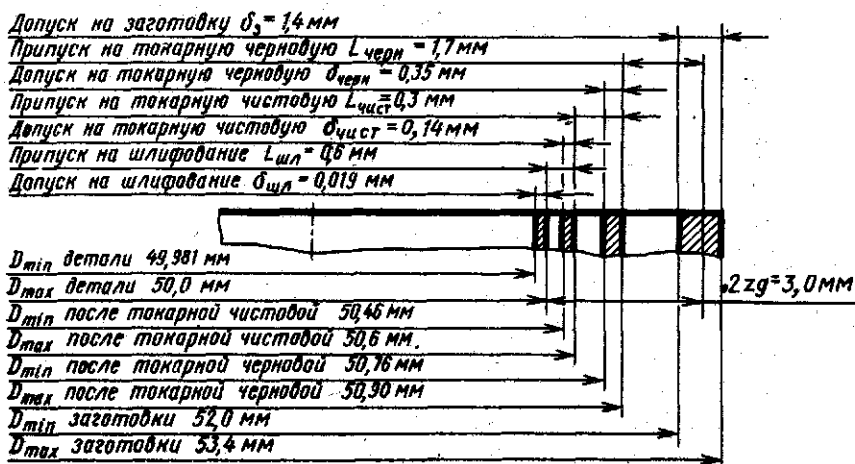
Пример расположения полей допусков и промежуточных размеров для операций
